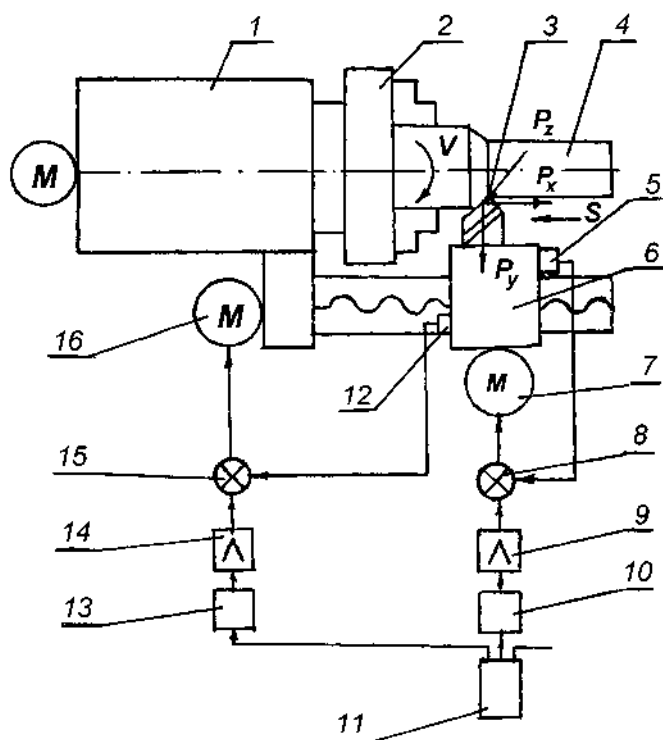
Схема, позволяющая повысить точность токарной обработки
